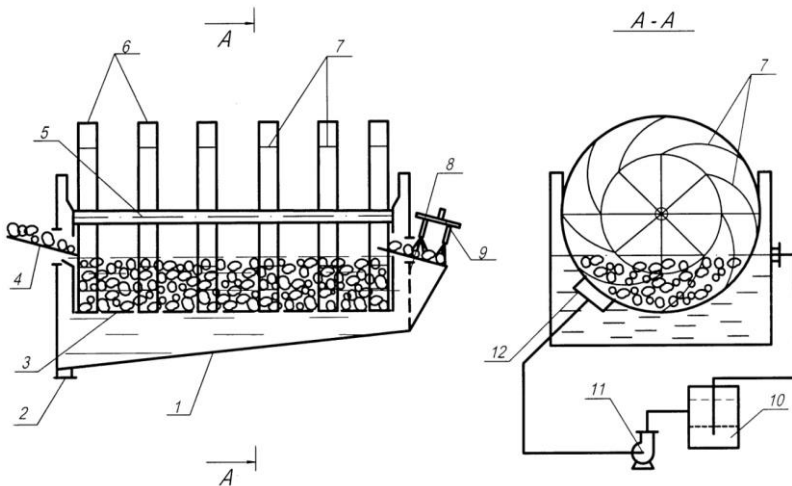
Схема барабанно-лопатевої мийки: 1-камера; 2- патрубок для видалення осілого бруду; 3 - мийна перфорована ванна; 4-ділянка завантаження; 5 - вал; 6 - циліндричні неширокі барабани; 7 – пластини; 8 - ділянка вивантаження; 9 - пристрій для ополіскування; 10 - ємність для фільтрування мийної води; 11 - насос; 12 - пристрій для подачі циркулюючої води
